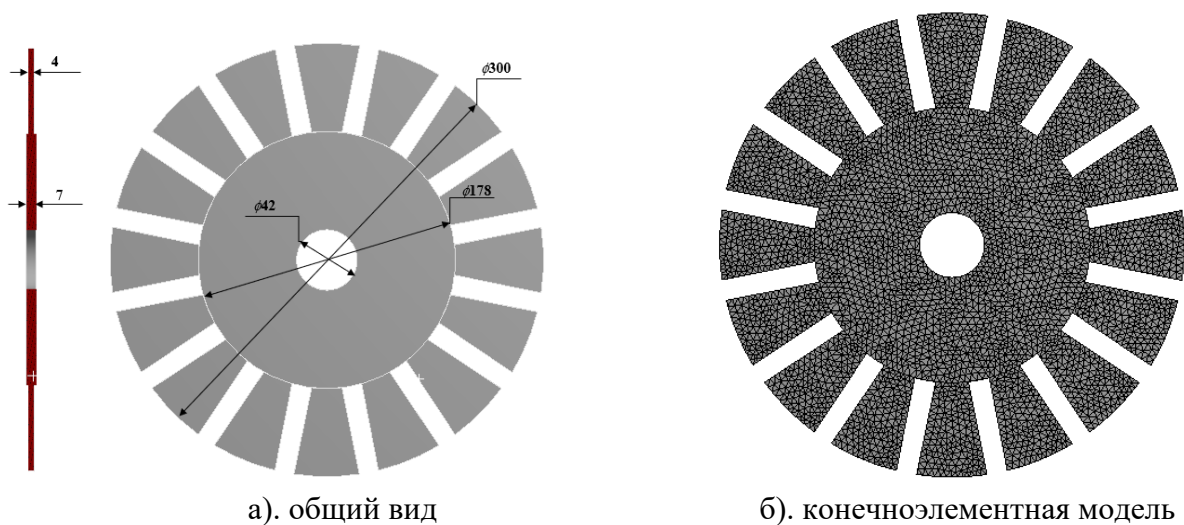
Рабочее колесо компрессора с 16-ю лопатками
